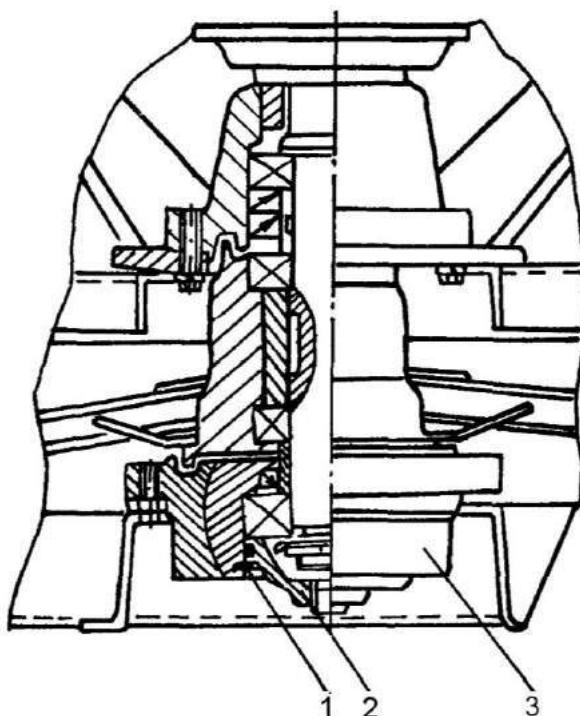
Схема смазки подборщика (ПКК 0350000)
